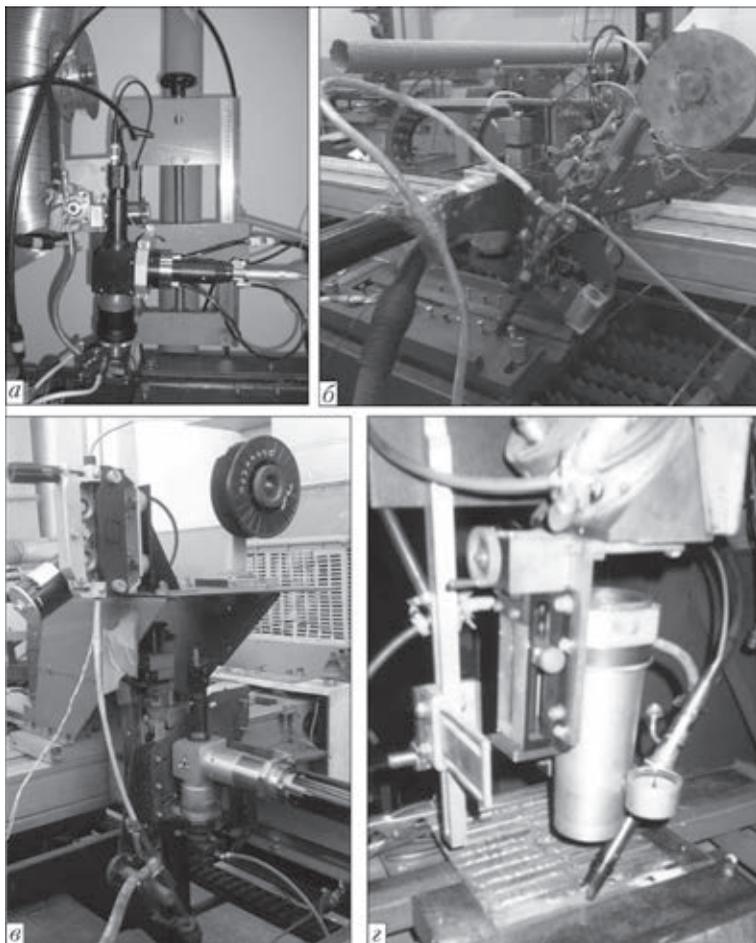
Внешний вид головок для гибридной лазерно-дуговой сварки, осуществляемой при помощи одно- или трехкоординатного манипулятора, разработанных в ИЭС им. Е.О. Патона: а-в — для лазеров с длиной волны до 1,06 мкм; г — 10,6
